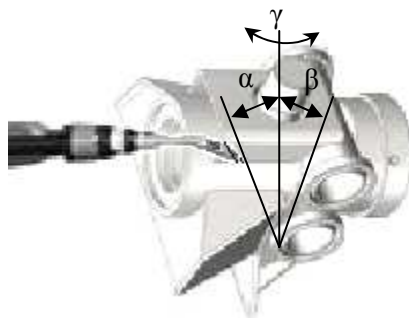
Общий вид сварной конструкции и углы ориентации технологического инструмента
